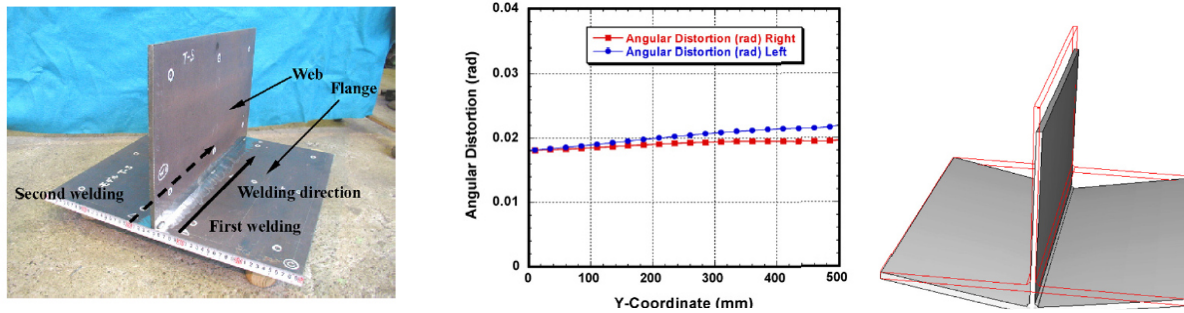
Soudure d'angle avec cordon de part et d'autre de la pièce soudée [DEN.07]
